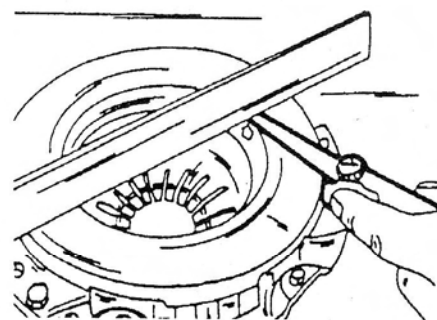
Контроль износа внутренней поверхности нажимного диска сцепления.
